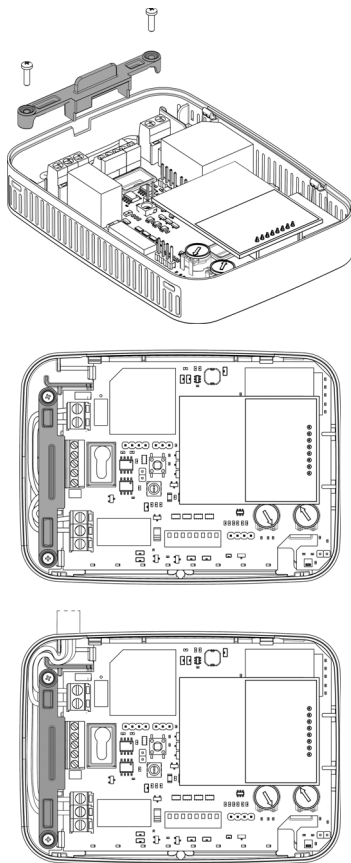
Retención cables / Cable retention / Fissaggio del cavo / Réention de câbles / Zugentlastung / Kabel borging / Upevnění kabelů
